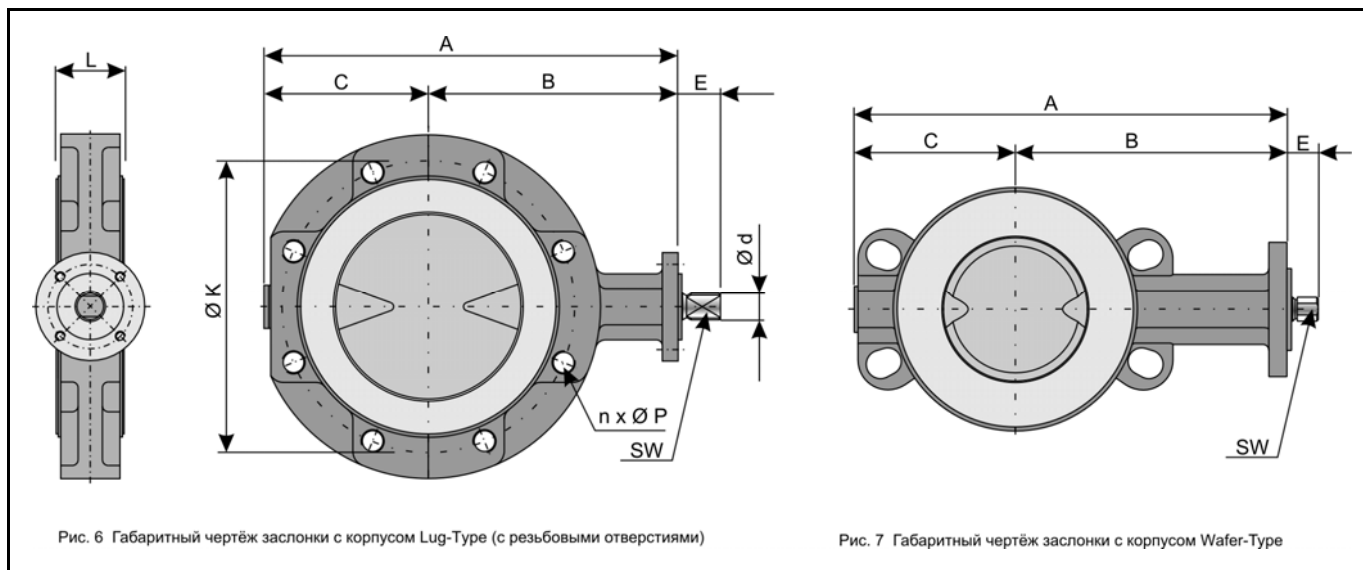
Габаритный чертёж заслонки с корпусом Lug-Type (с резьбовыми отверстиями)
